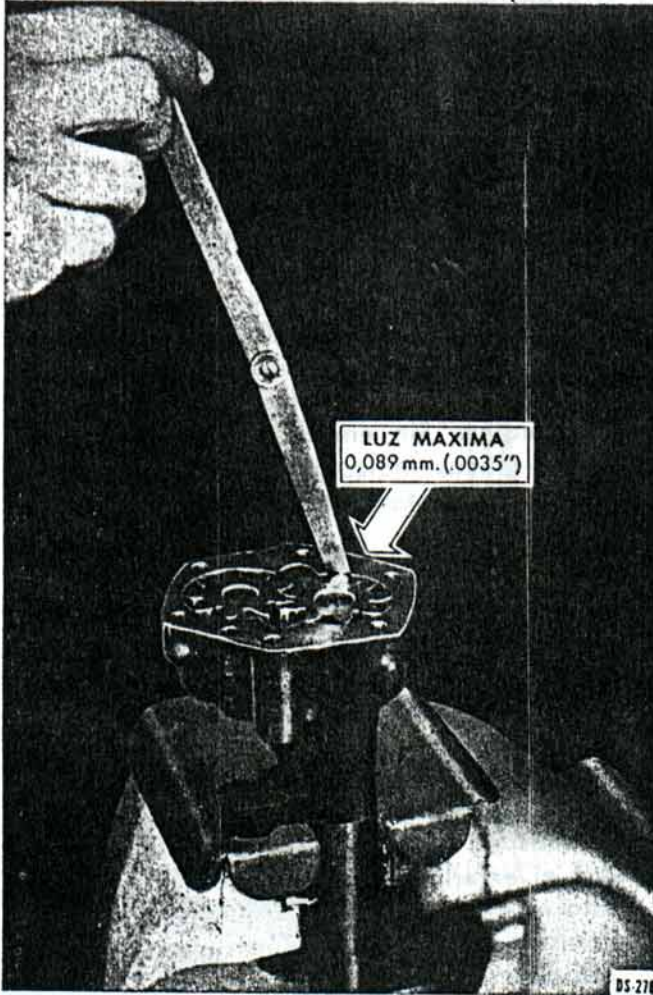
Verificando la luz entre el cuerpo de la bomba y el diente del engranaje.
